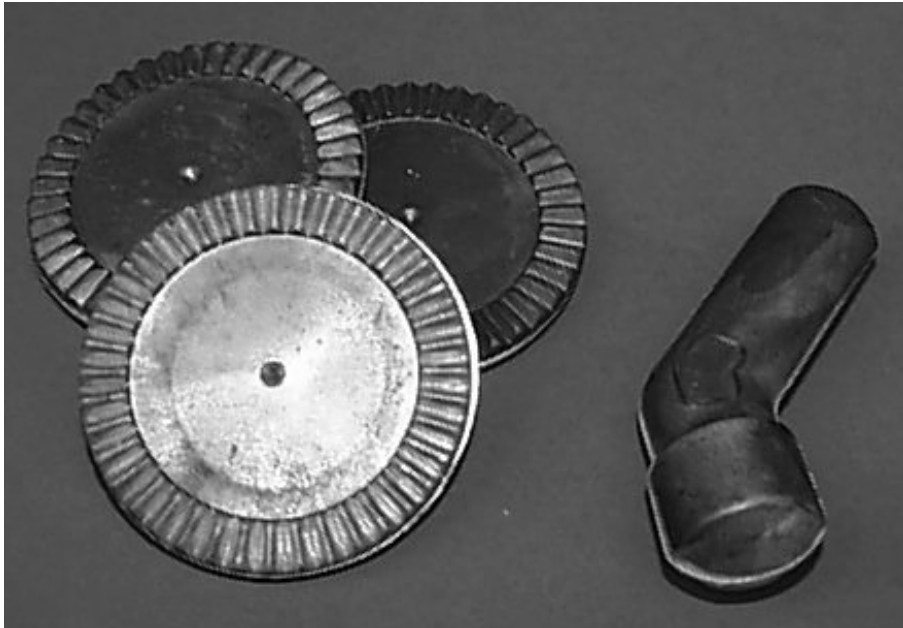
Gesenkgeschmiedete Rollstuhlkomponente (links, Durchmesser 62 mm) und Winkelstück (rechts, Länge 79 mm) aus AZ31, Werkzeuge der Firma WICHARD, Frankreich
